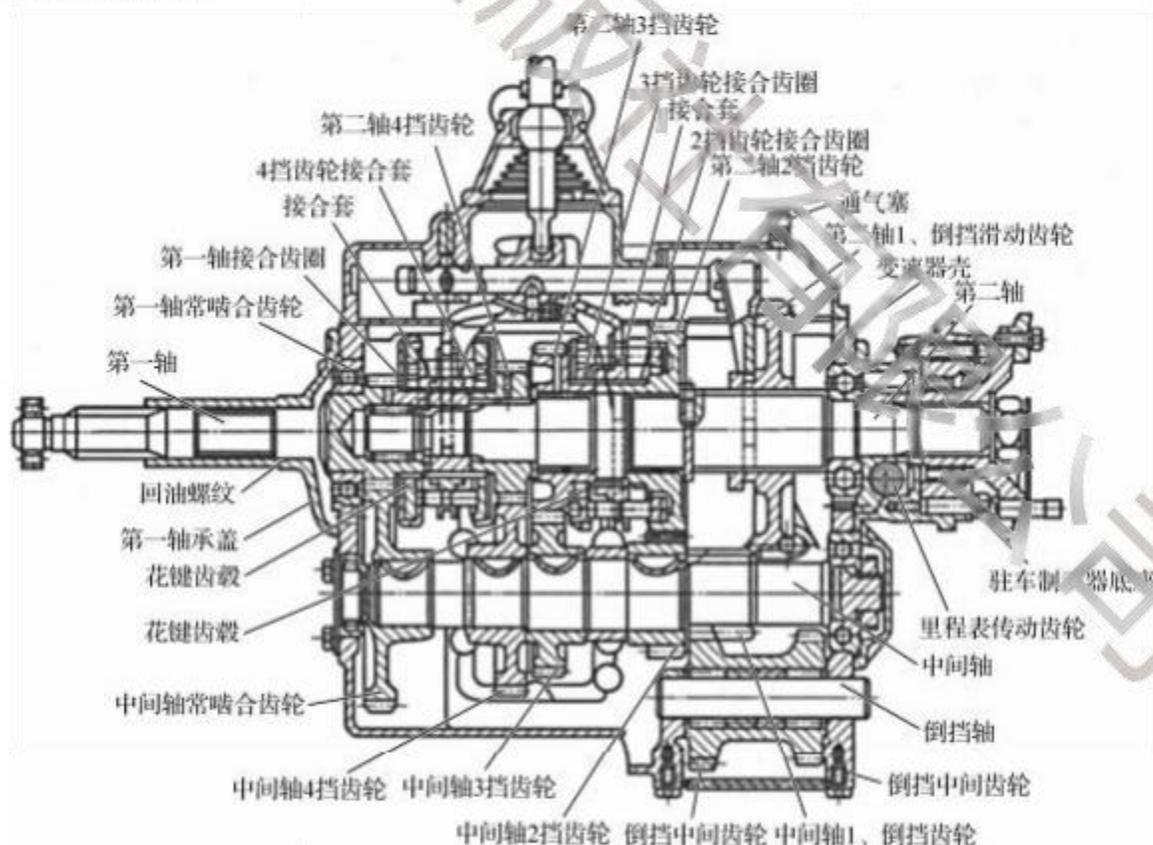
典型的 3 轴式 5 挡普通齿轮变速器的结构
